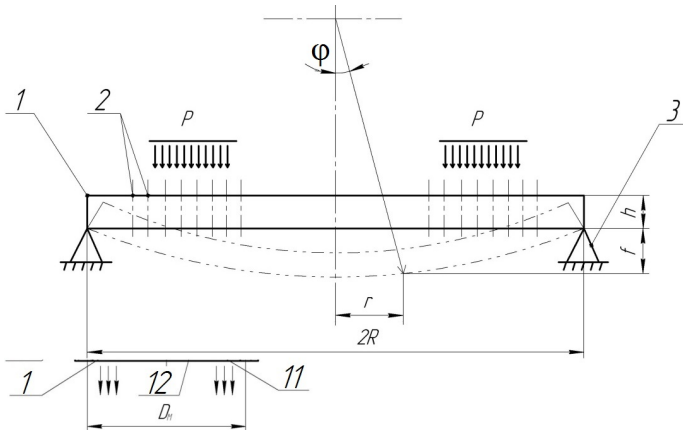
Схема деформаций корпуса сплошной матрицы с шарнирным закреплением по наружному контуру:
